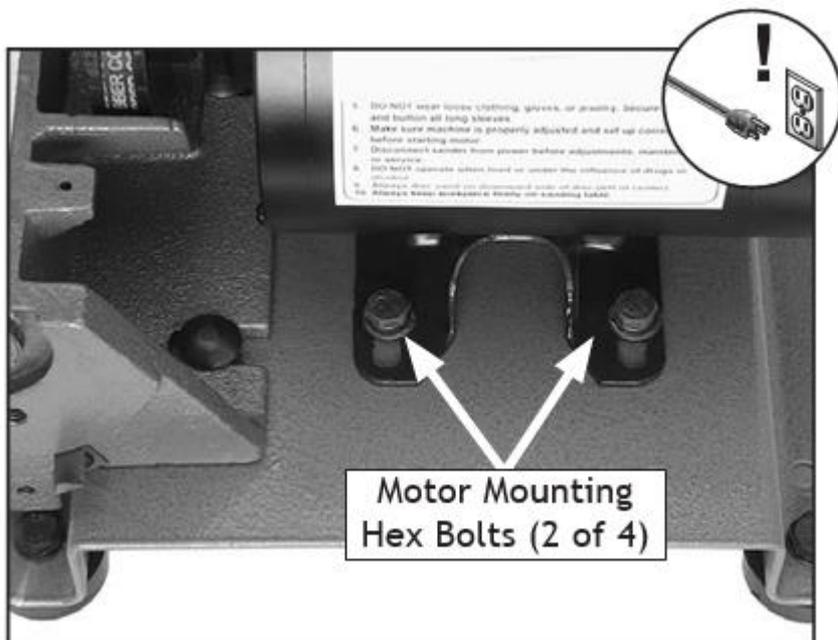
Болты с шестигранной головкой для крепления двигателя (2 из 4, если смотреть сверху).
